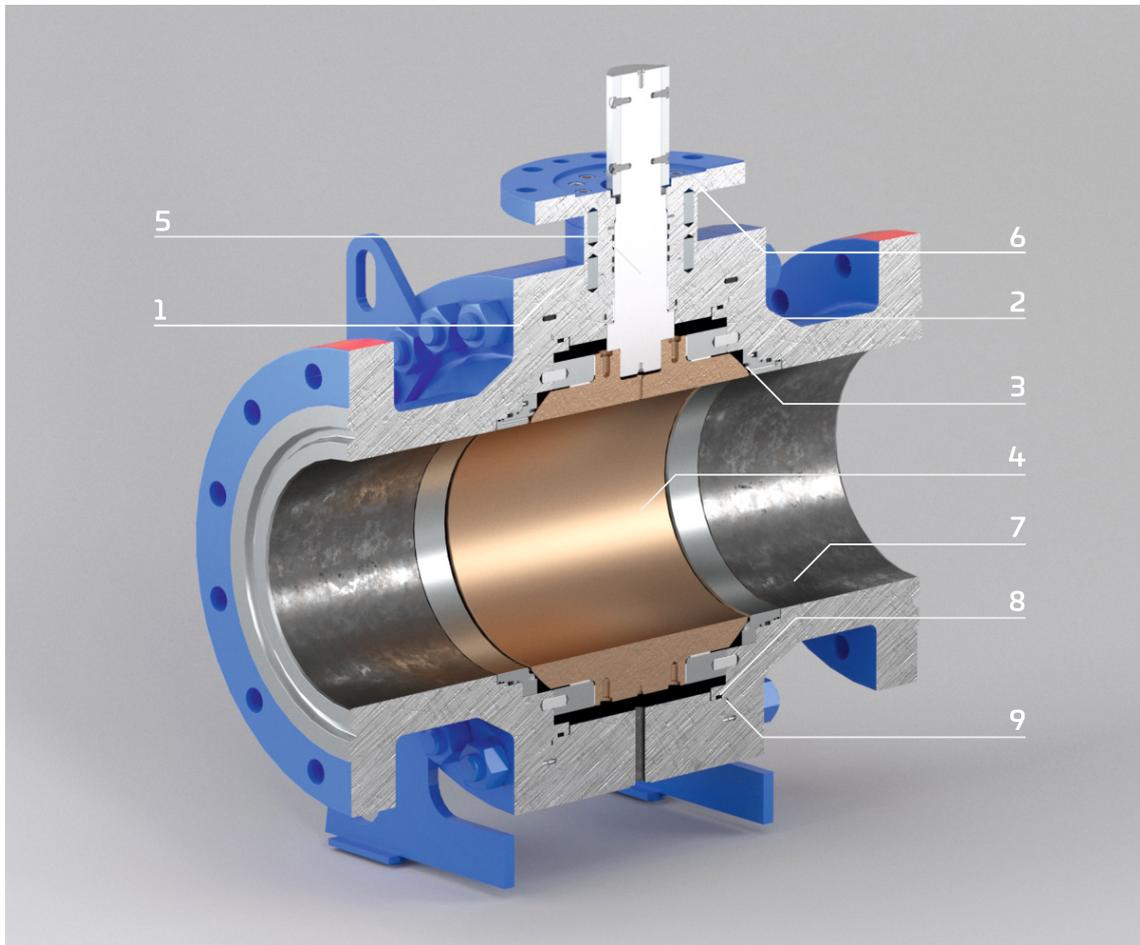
Кран шаровой стандартный в разборном корпусе.
